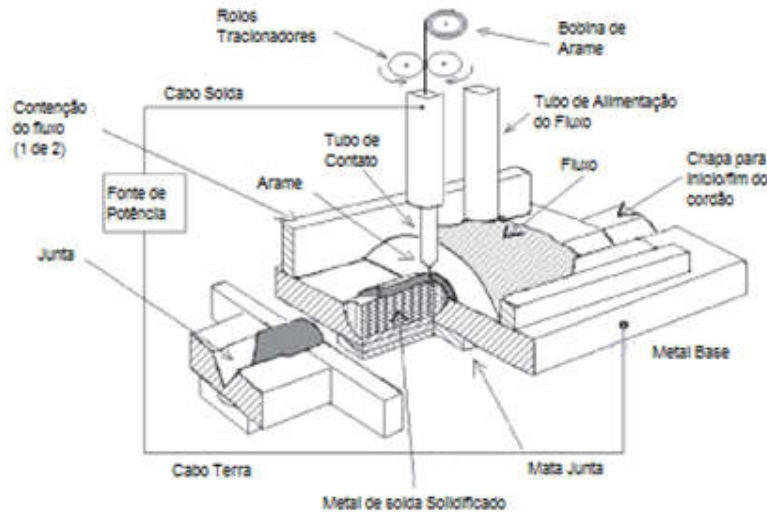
Equipamento para a Soldagem ao Arco Submerso
